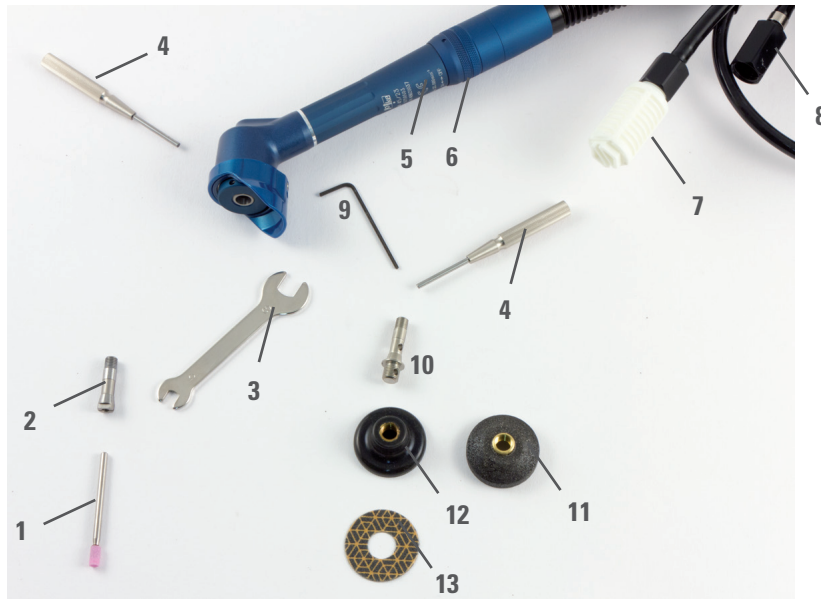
Vue d'ensemble des machines de meulage turbo à main G 90/23 et W 45/23
